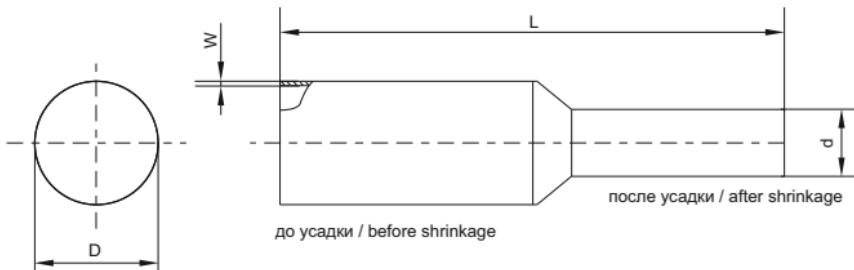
Габаритные размеры ТТУ / Figure 1 – Overall dimensions of TTU
